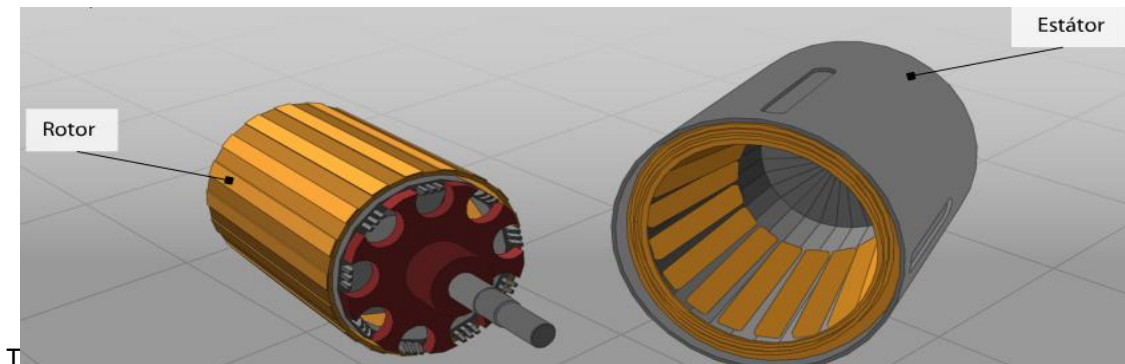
Estator y rotor de motor trifásico jaula de ardilla
